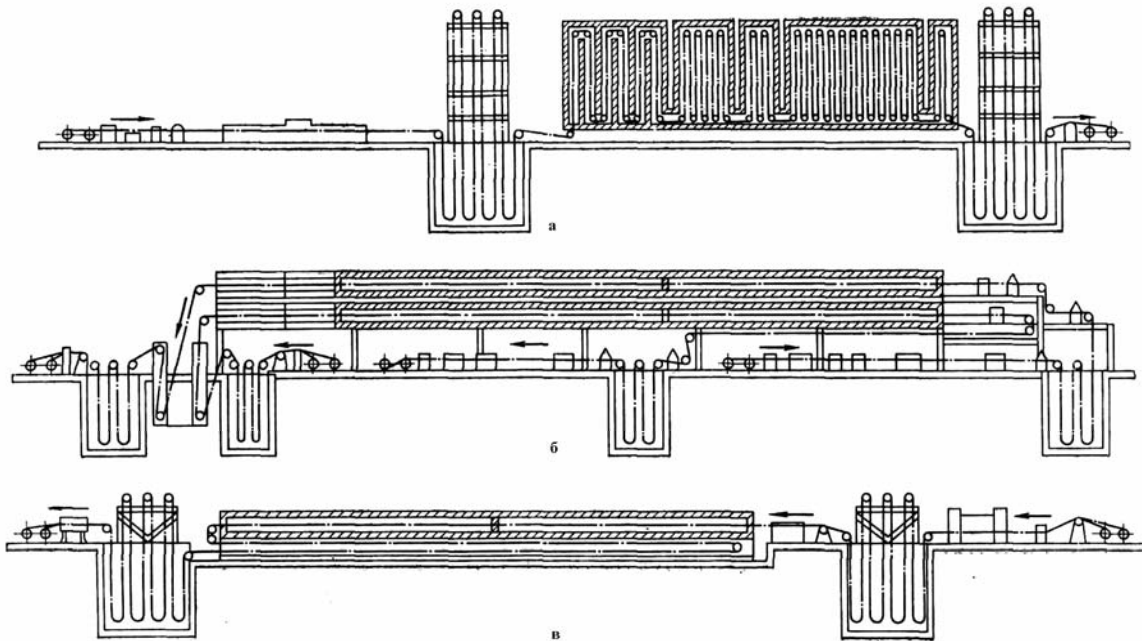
Агрегати для обробки трансформаторної сталі
